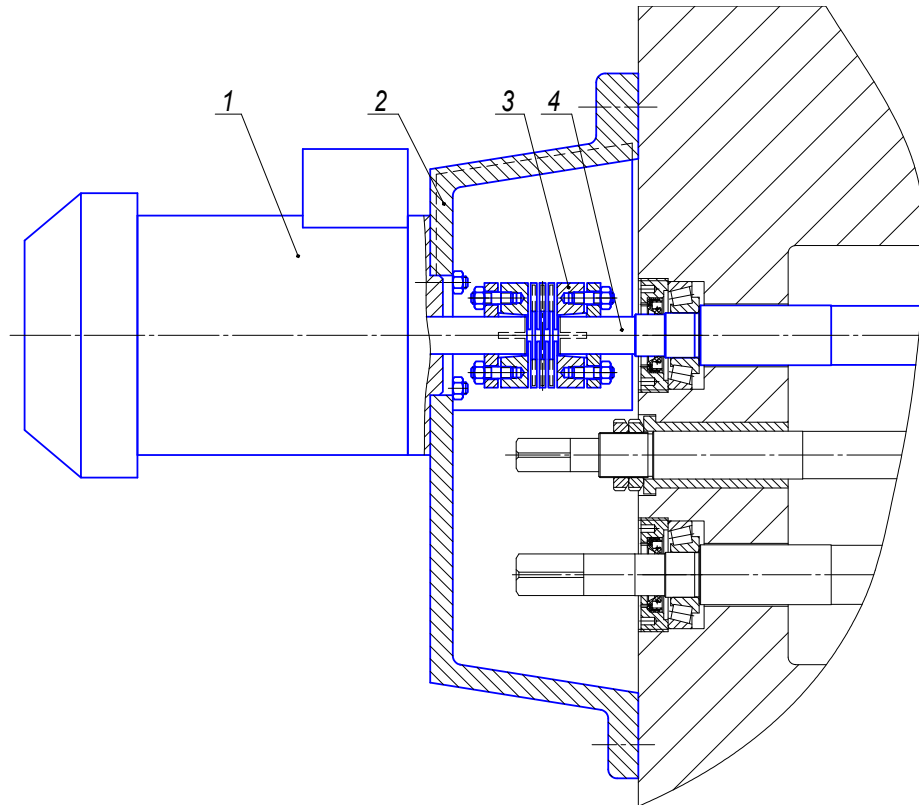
Привід поперечних подач фрезерувальної бабки
